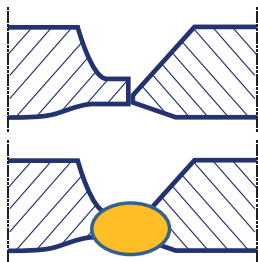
Сварной шов, нижнее положение – верхнее фото, потолочное положение – нижнее фото
